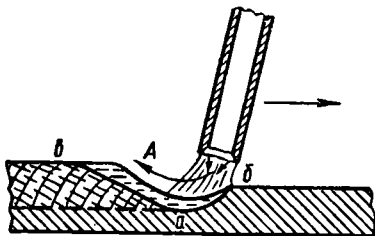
Схематическое изображение продольного сечения сварочной ванны первого типа.
